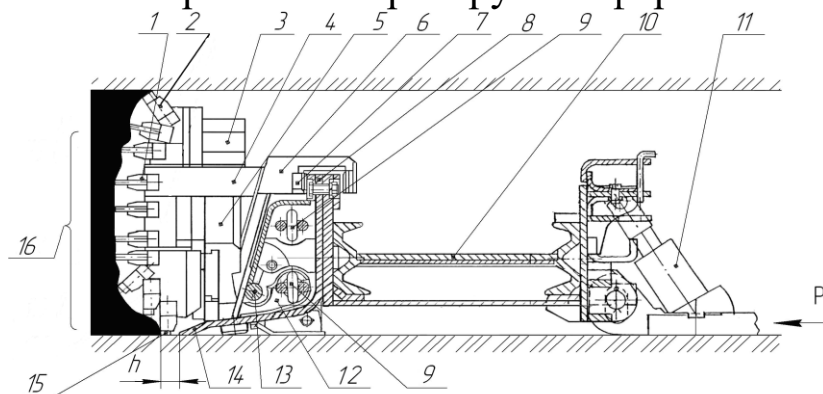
Разрез по корпусу исполнительного органа струговой установки 2СН3413 скользящего типа:
